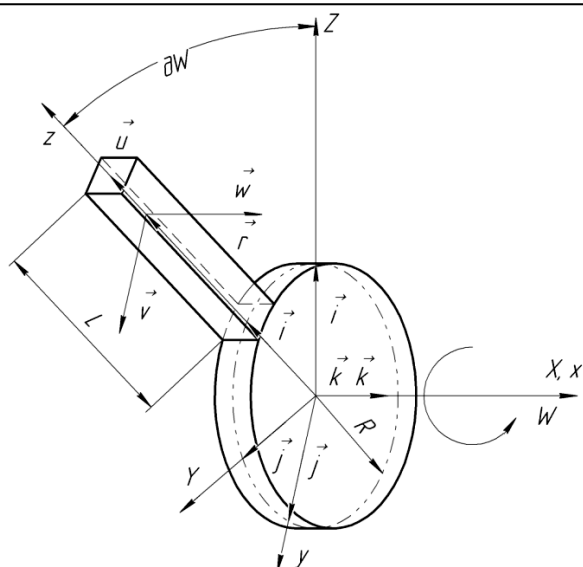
Розрахункова схема механічної полімерно-абразивної щітки
